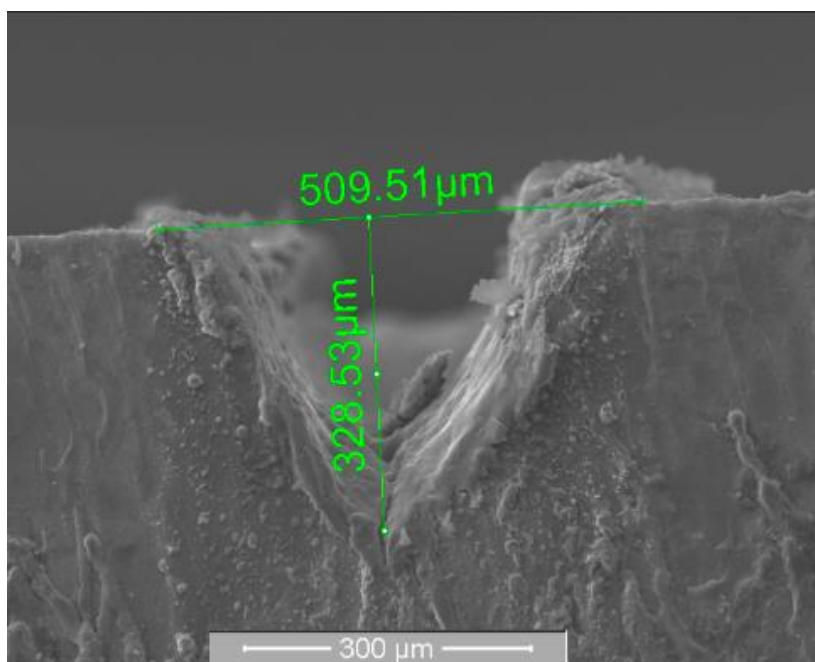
Профиль на торце образца из стали AISI 304 с параметрами для получения резьбового соединения M2
